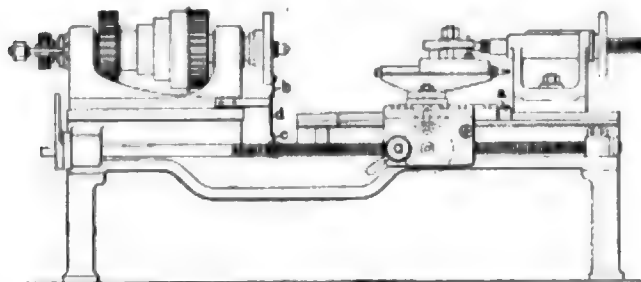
Z. A. Gewindeschneiderfahren für Spindeln und lange Schrauben.
